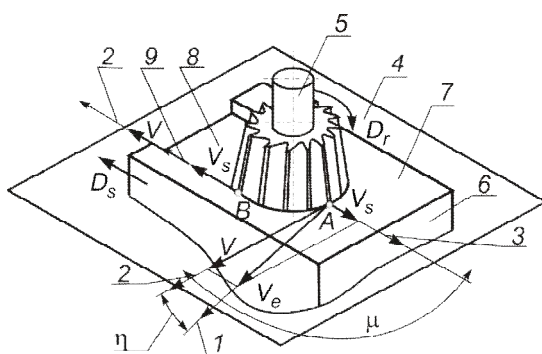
Элементы движений в процессе резания при торцевом фрезеровании:
